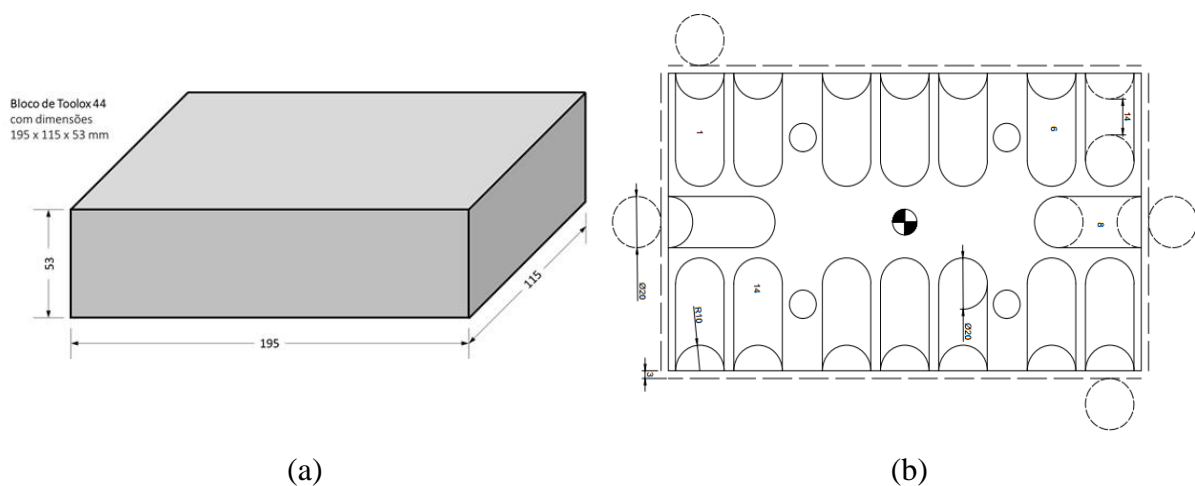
Desenho esquemático: (a) corpo de prova; (b) planejamento da usinagem.
